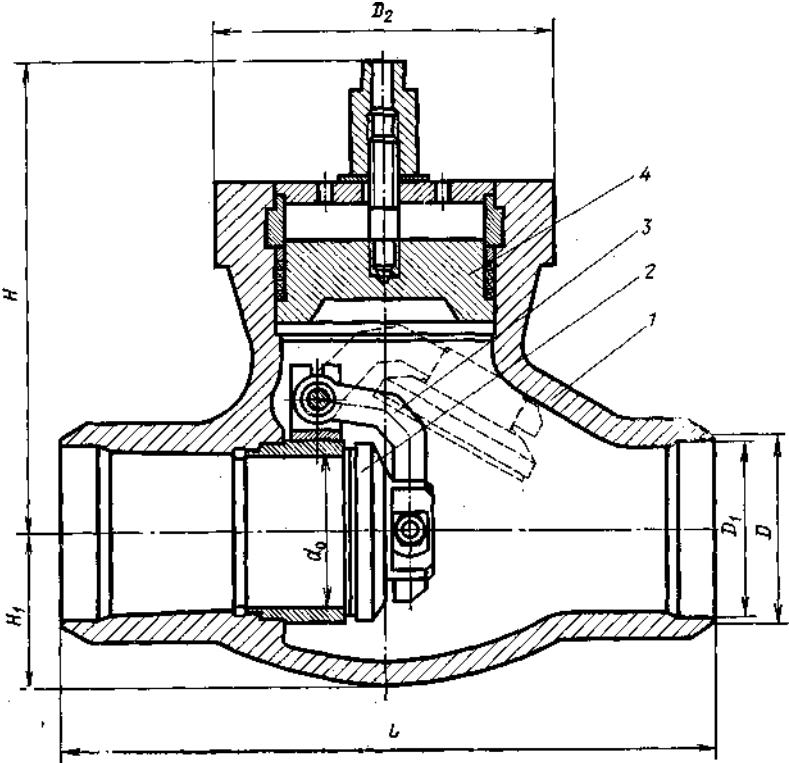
Обратный клапан поворотный Т-122 и Т-123
